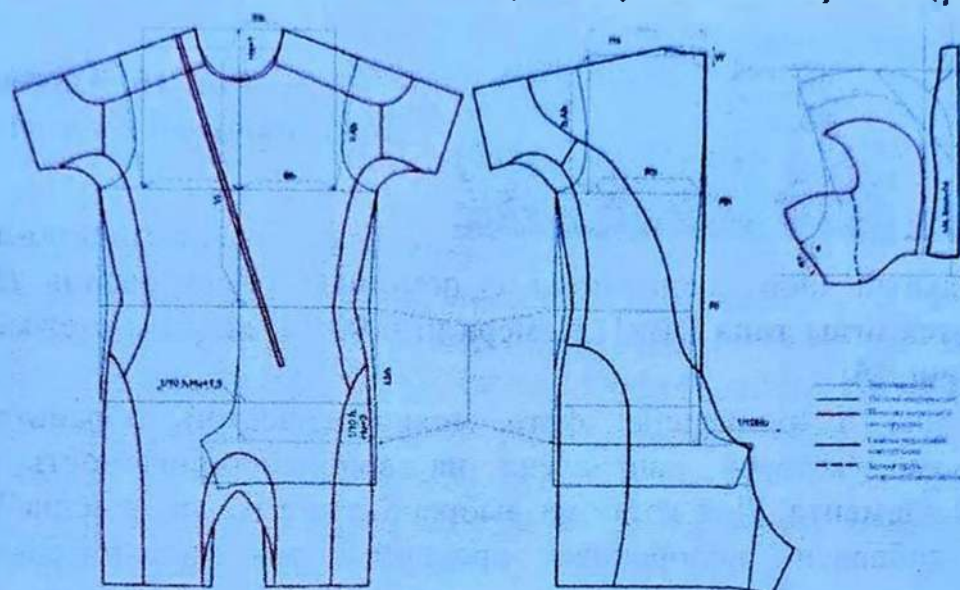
Чертёж базовой и модельной конструкции гидрокостюма
